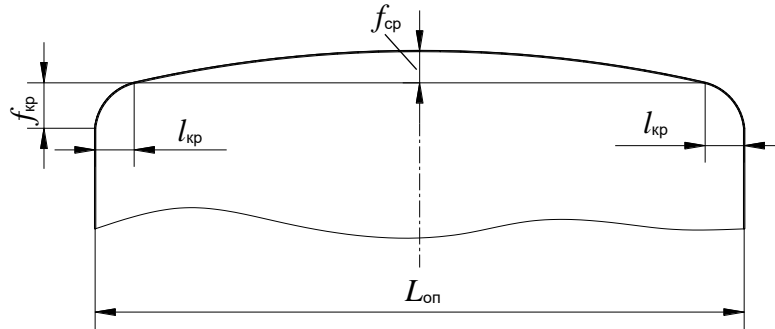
Предлагаемая профилировка опорного вала
